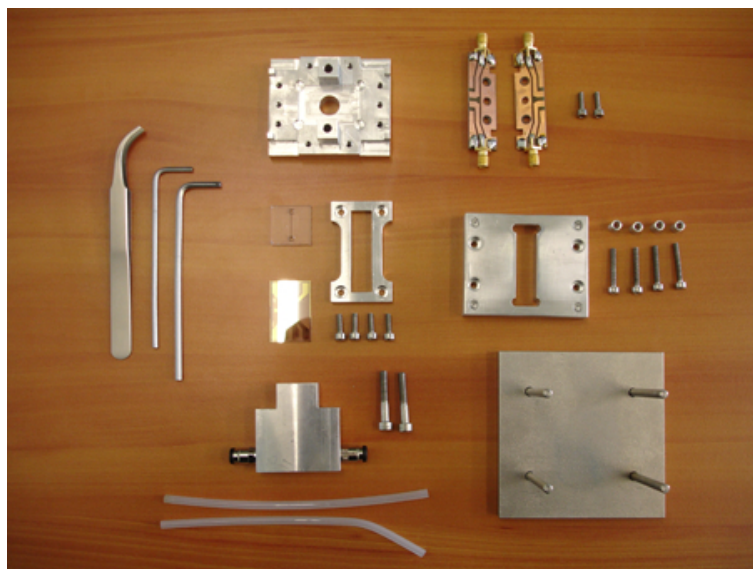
Ensemble de toutes les pièces et outils nécessaires pour assembler le système *Liquichip*.
